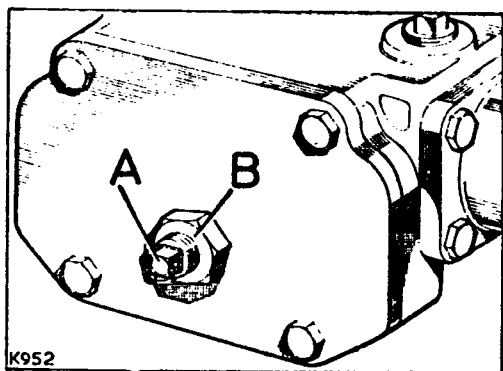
Tornillos de ajuste de la caja de engranajes.
